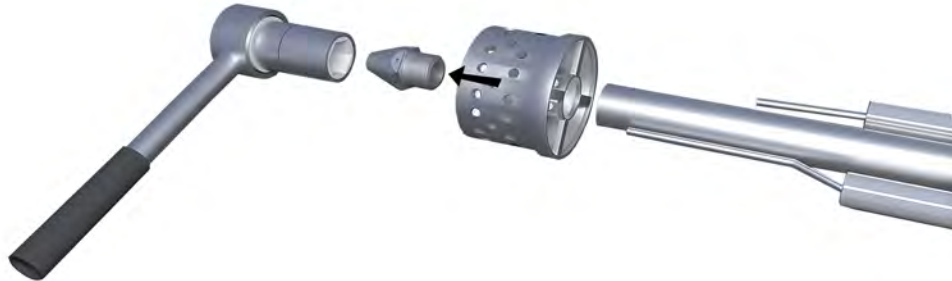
Etape 5 Remplacer les pièces d'usure du brûleur d'allumage
